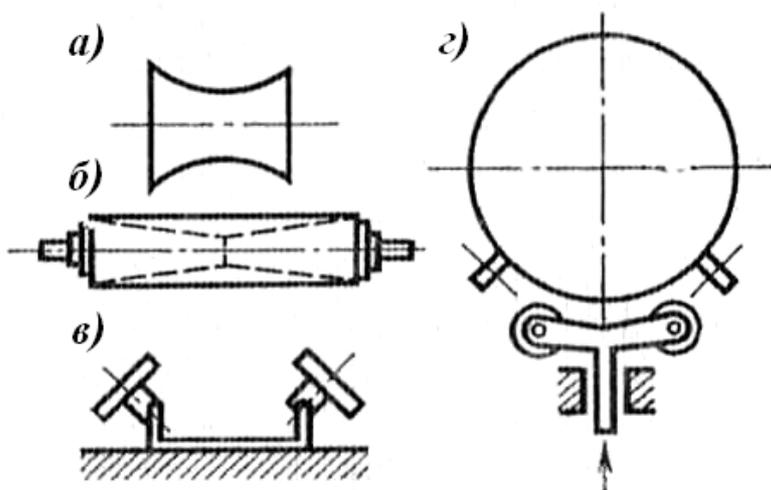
Схемы роликовых конвейеров для цилиндрических заготовок
